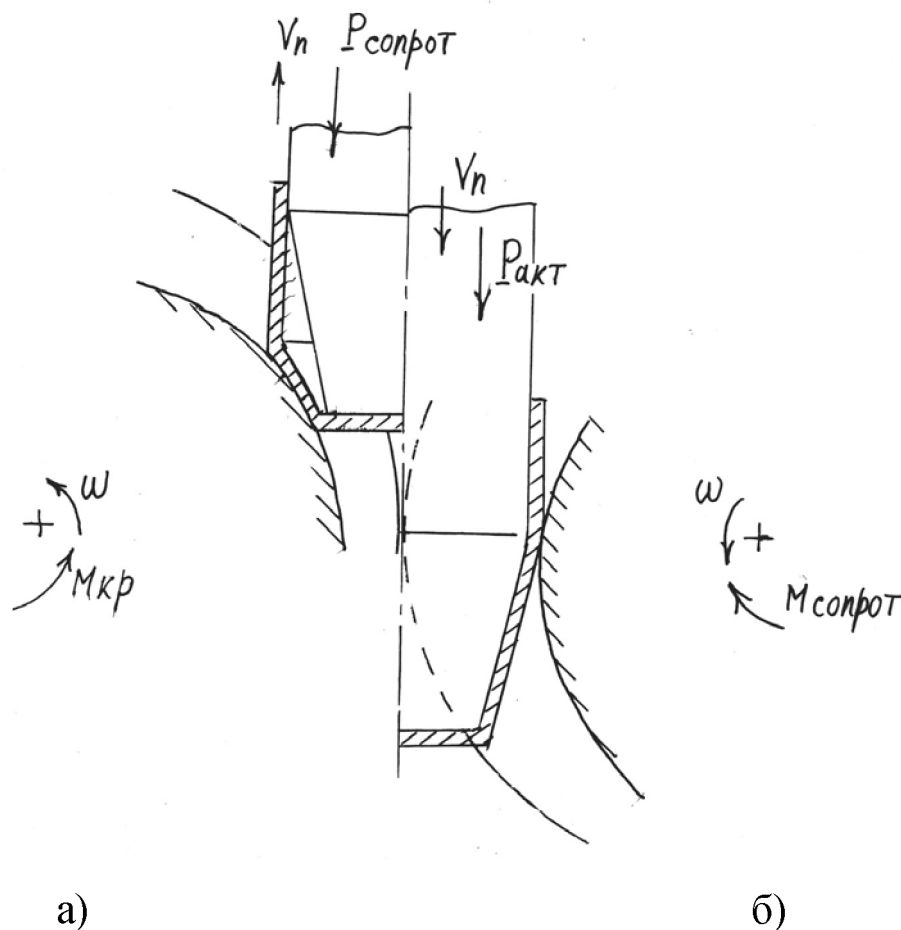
Схема вытяжки рассматриваемой детали через валцы
